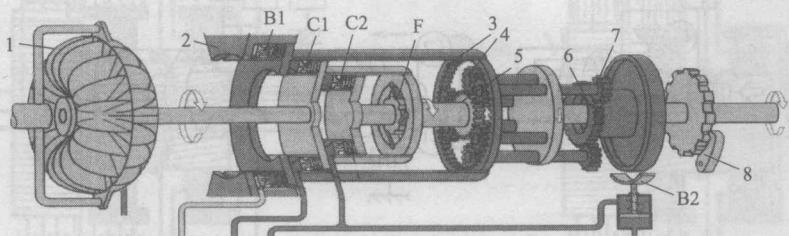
拉威娜式三速行星齿轮变速器的结构简图
